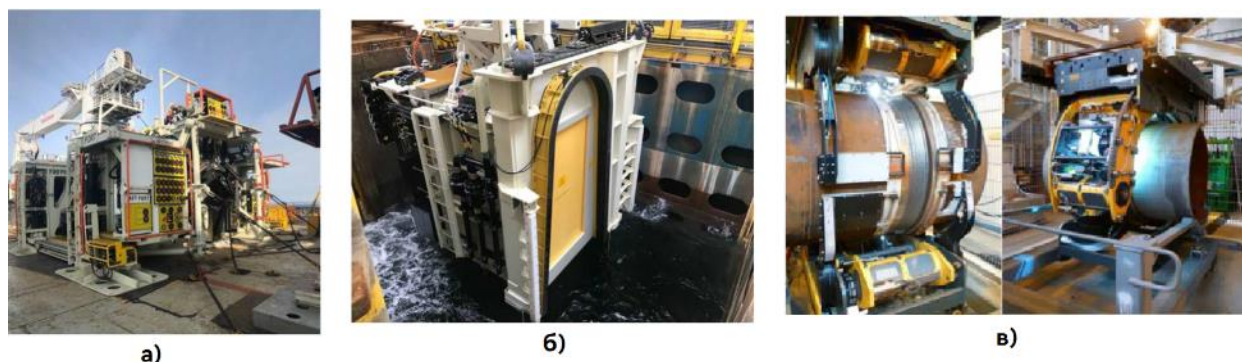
Основные сварочные модули на месторождении «Йонес Свердруп» [2]
